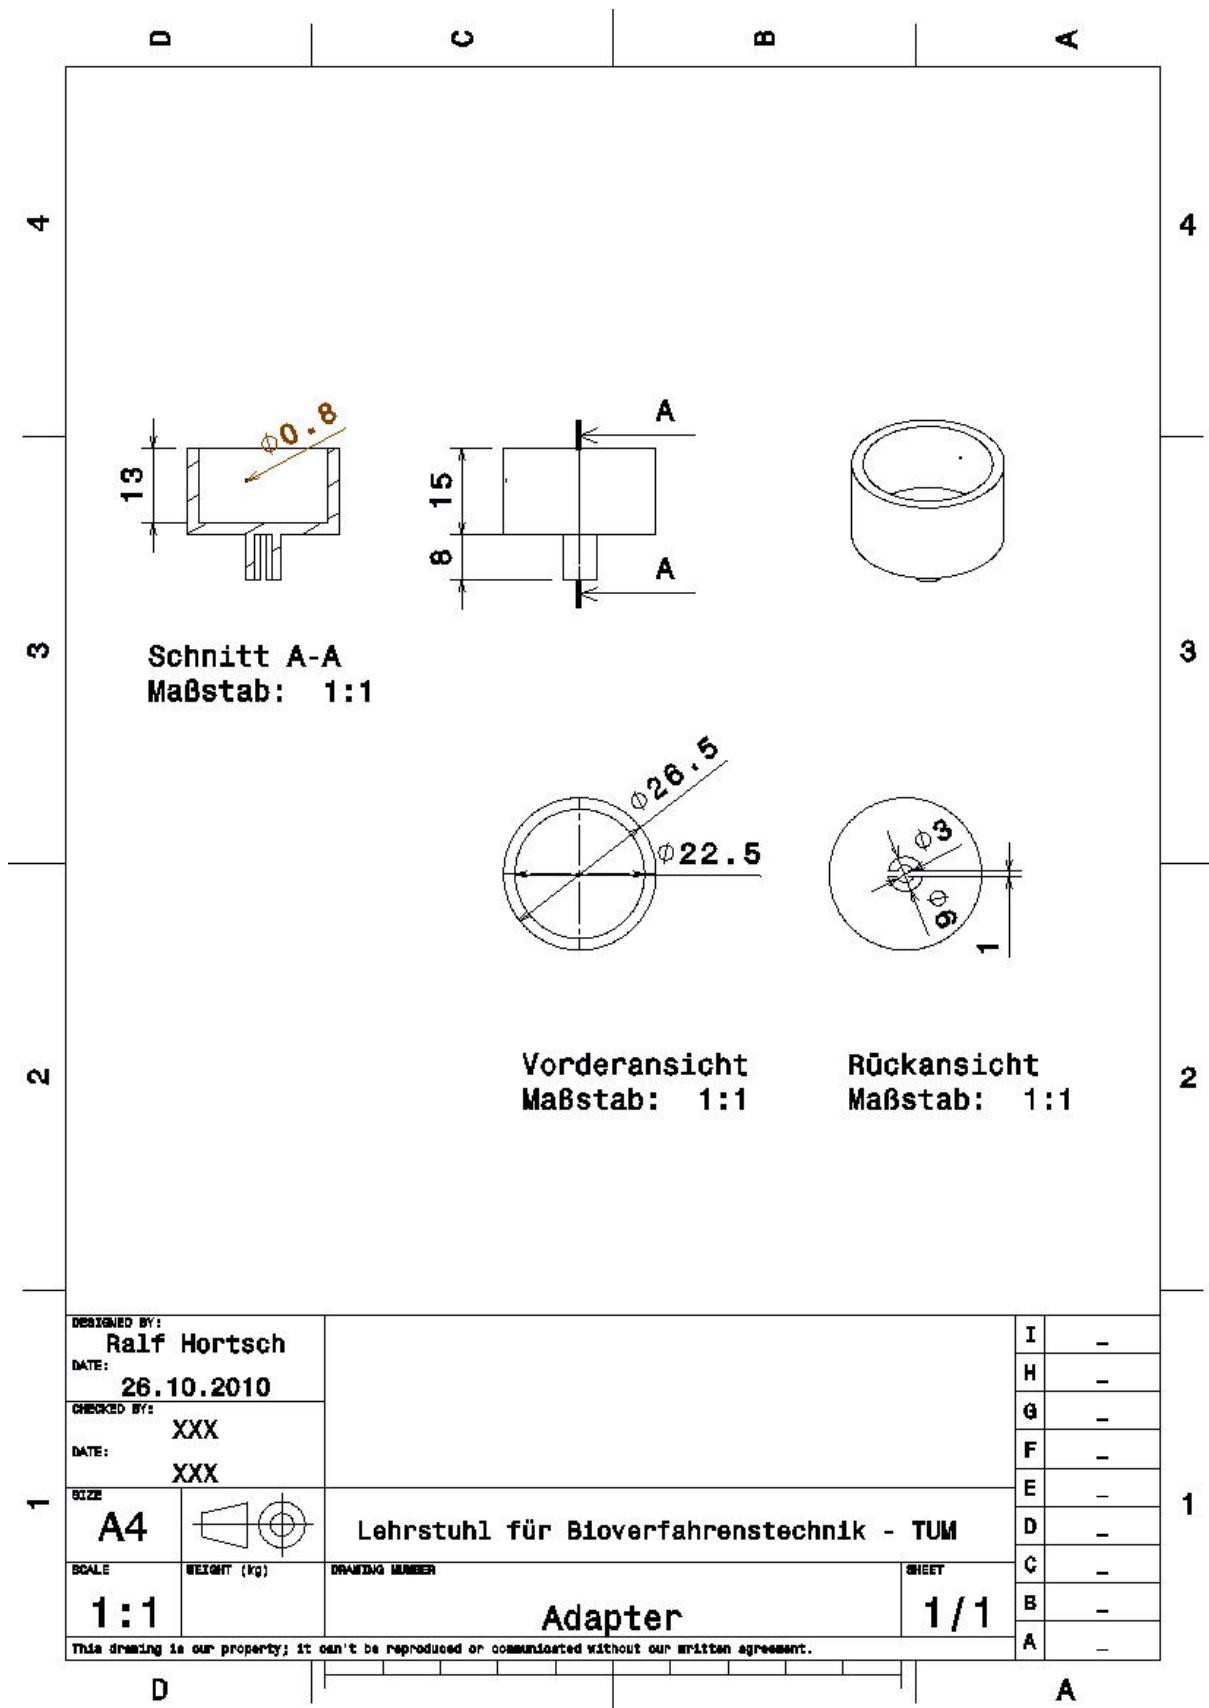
Technische Zeichnung des zur Messung des Leistungseintrags im mL-Bioreaktor verwendeten Adapters.
